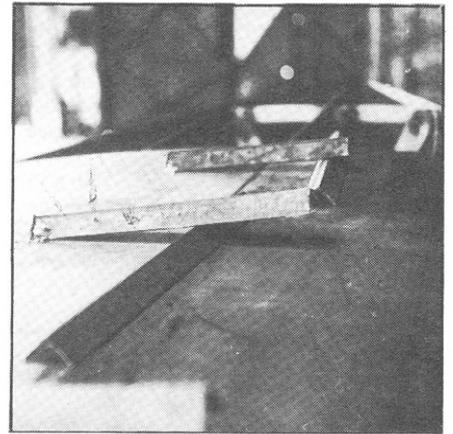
Fers plats servant de leviers pour amener une tôle à sa place.
